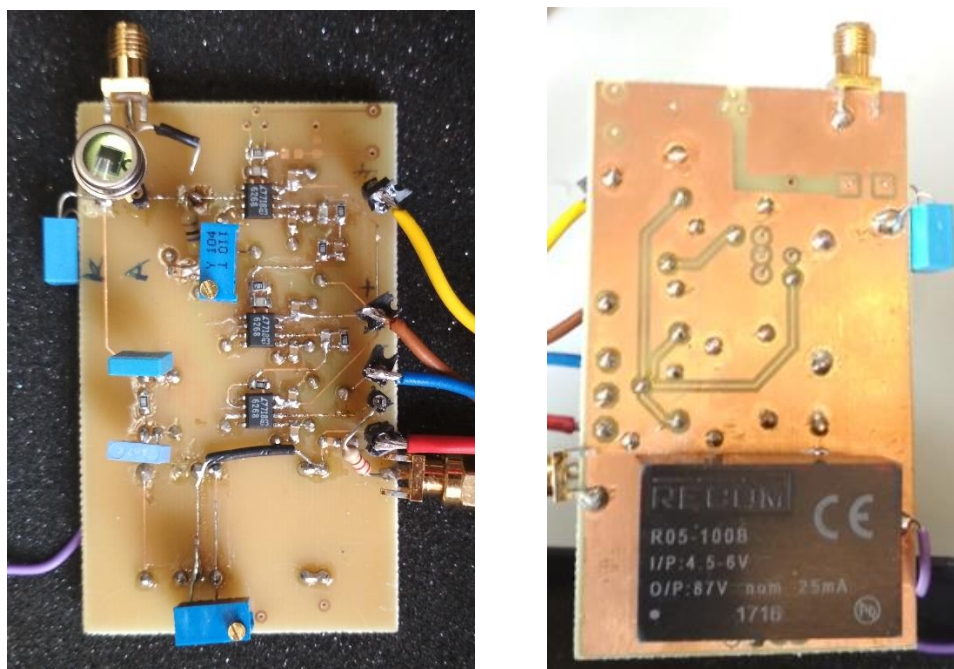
Prototipo fabricado cara TOP a la izquierda y BOTTOM a la derecha
